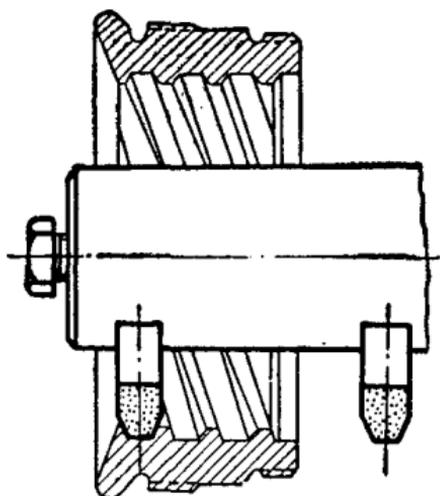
Борштанга для нарезания внутренней двухзаходной резьбы.
